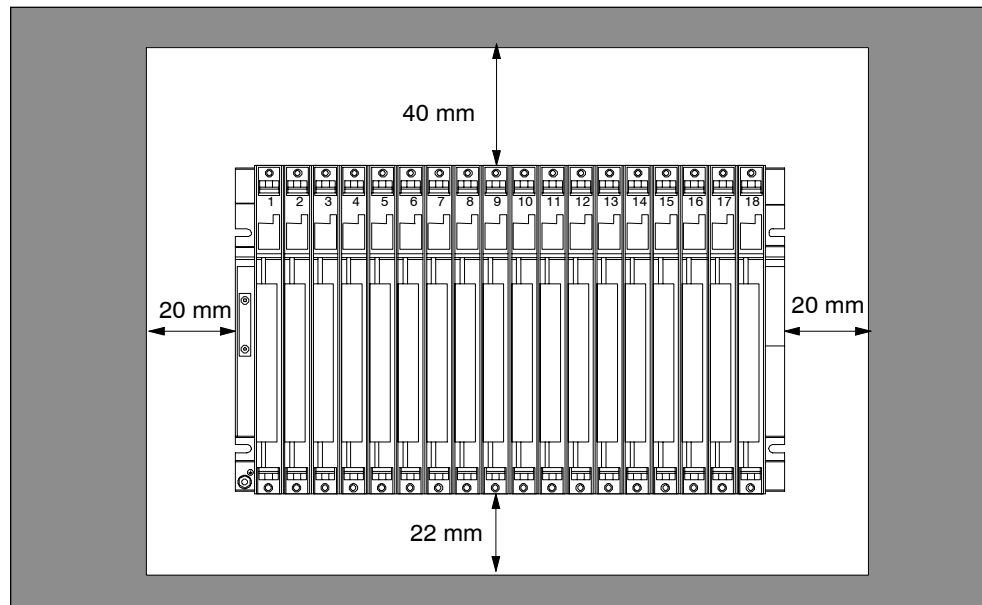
Mindestabstände beim Aufbau einer S7-400
